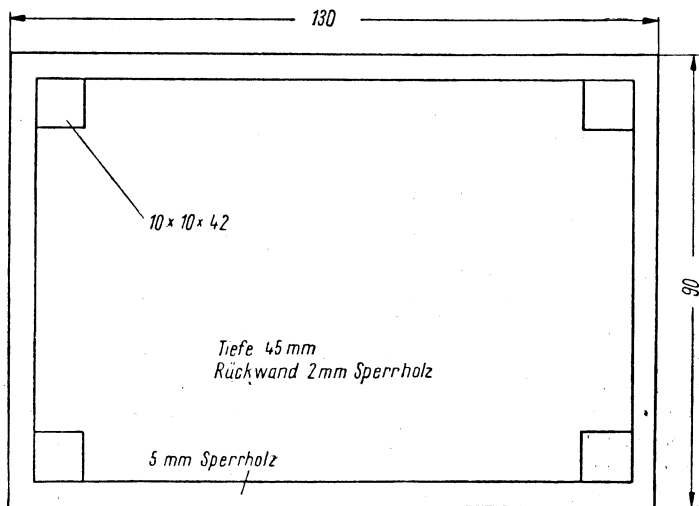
Maßskizze für das Holzgehäuse des Durchgangsprüfers
